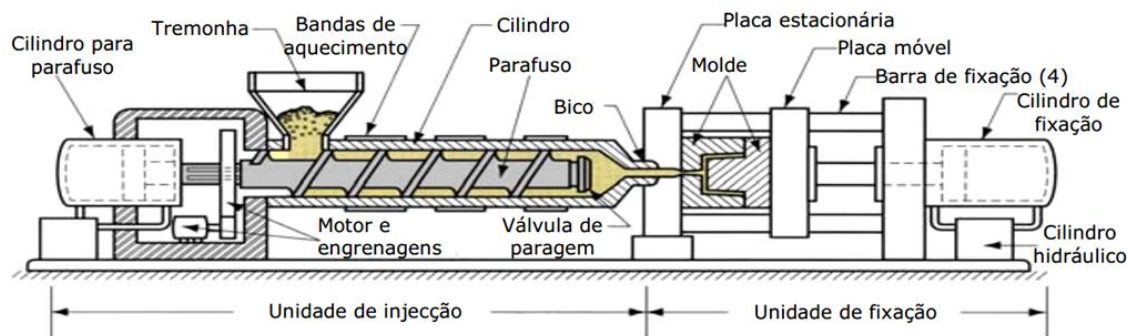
Esquema representativo de uma máquina de moldação por injeção (Universidade Técnica de Lisboa).
